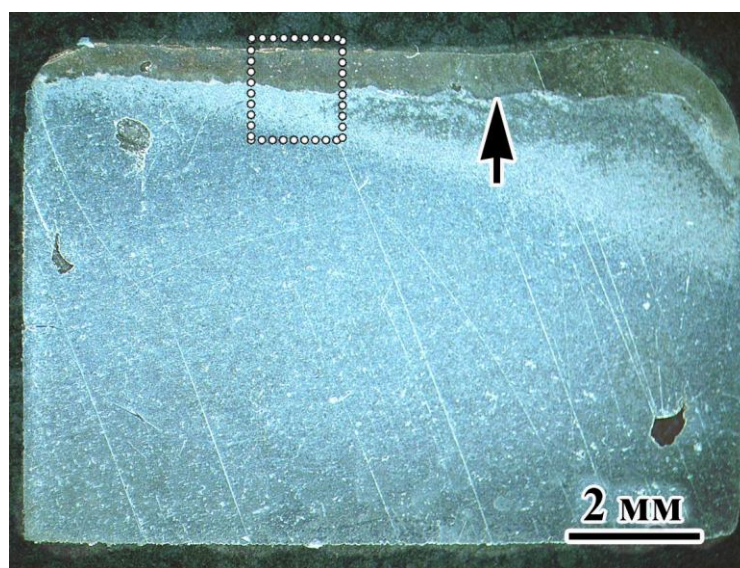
Поперечний переріз лазерно-оплавленого зразку
